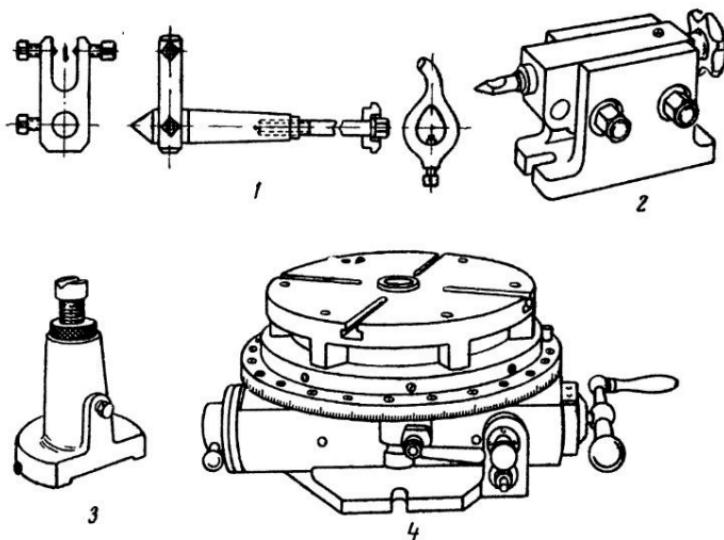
Некоторые приспособления к фрезерному станку: 1 — по-водковый центр с хомутиком; 2 — задняя бабка; 3 — домкратик; 4 — поворотный стол.
